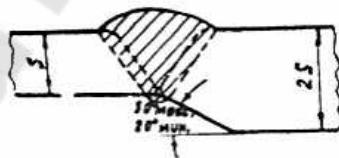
Подготовка для сварки торцов труб с разной толщиной (δ) стенки
